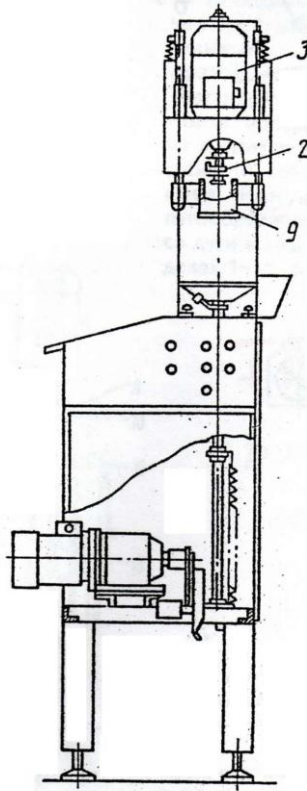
Пристрій для очищення головок капусти, вигляд з боку
